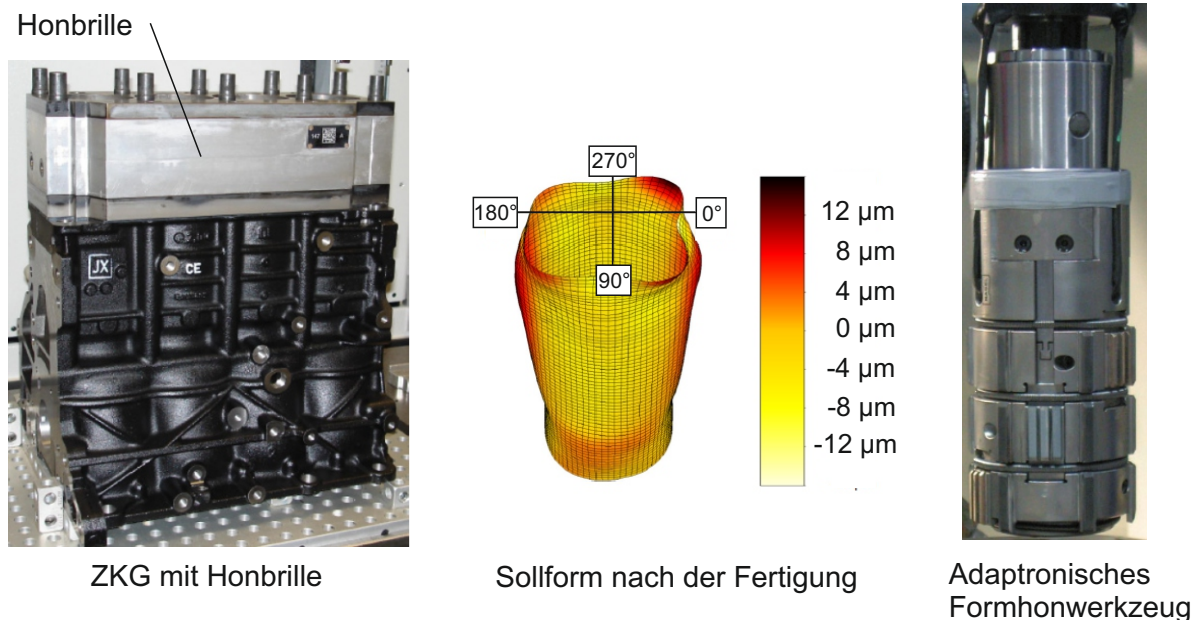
Links: Zylinderkurbelgehäuse mit Honbrille vorgespannt, Rechts und Mitte: Formhonwerkzeug mit errechneter Sollform [Schn11, Schn12]
